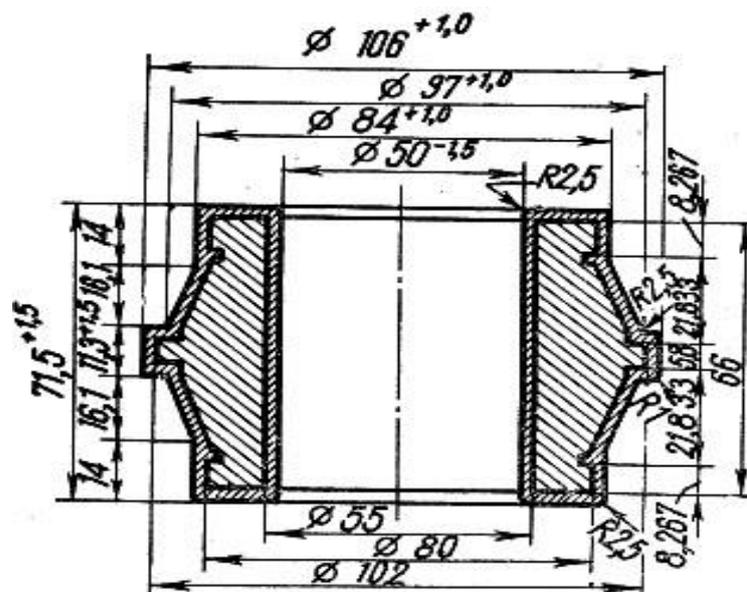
Заготовка внутрішнього кільця підшипника у вигляді штамповки
